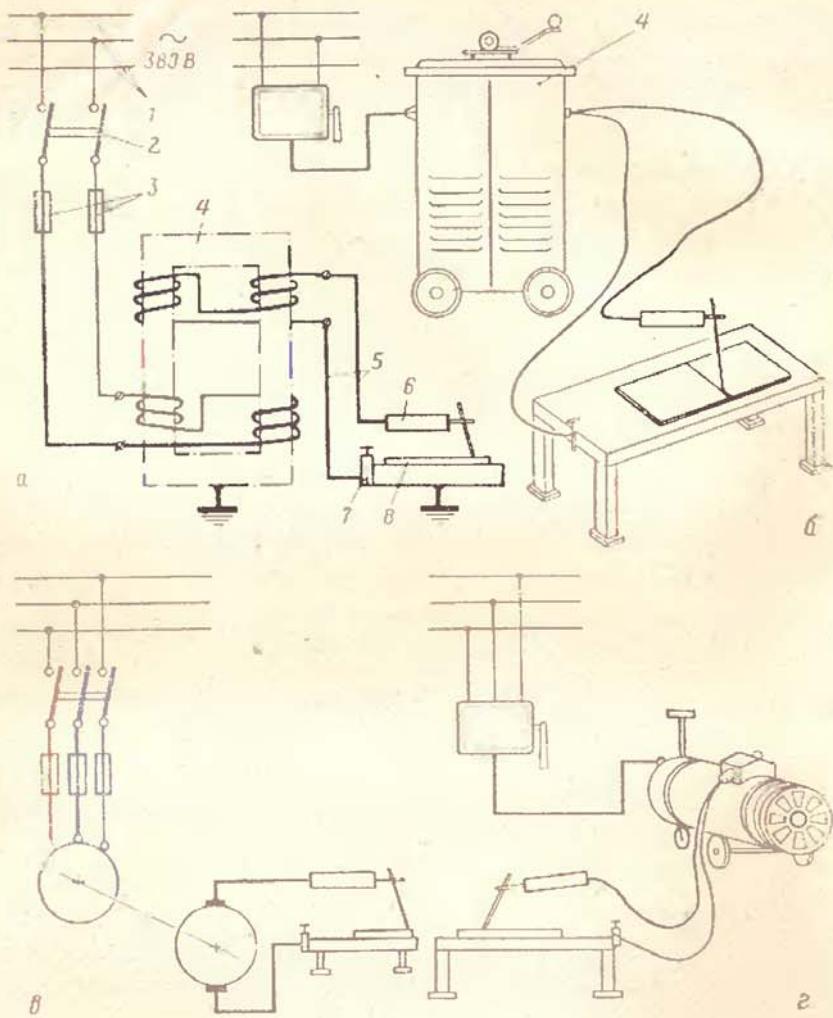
Принципиальные электрические и монтажные схемы поста для ручной дуговой сварки:
